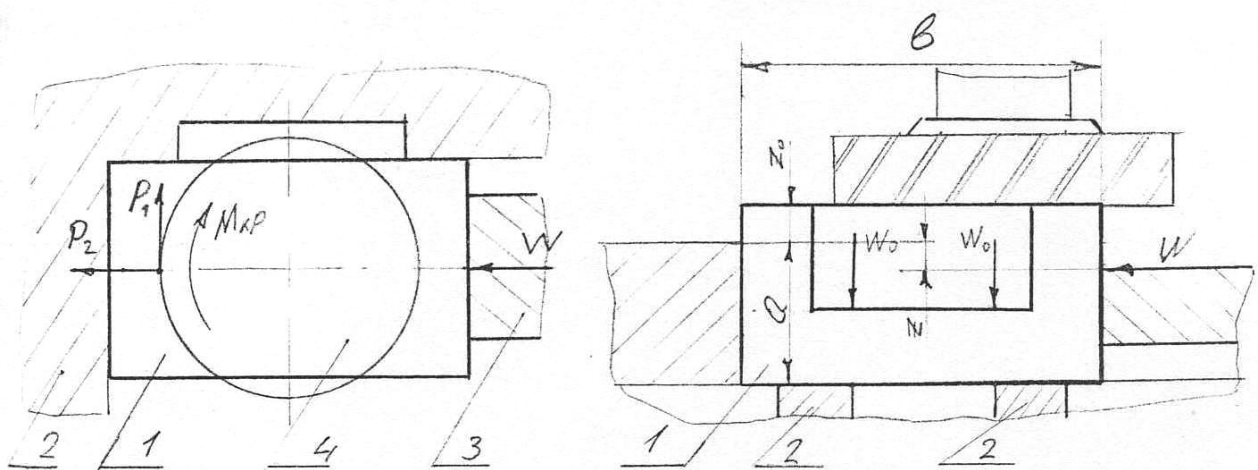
Розробка схеми закріплення: - деталь, 2 - опорні елементи, 3 - прихвати, 4 - торцева фреза.
